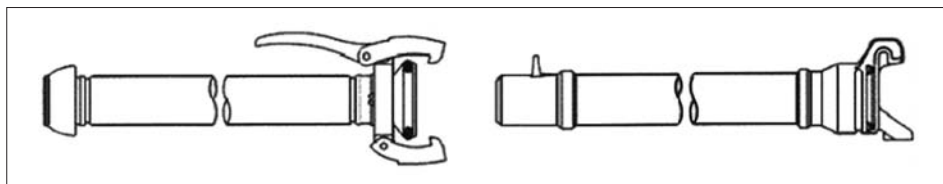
Junta de palanca (izquierda), y junta hidráulica (derecha).
